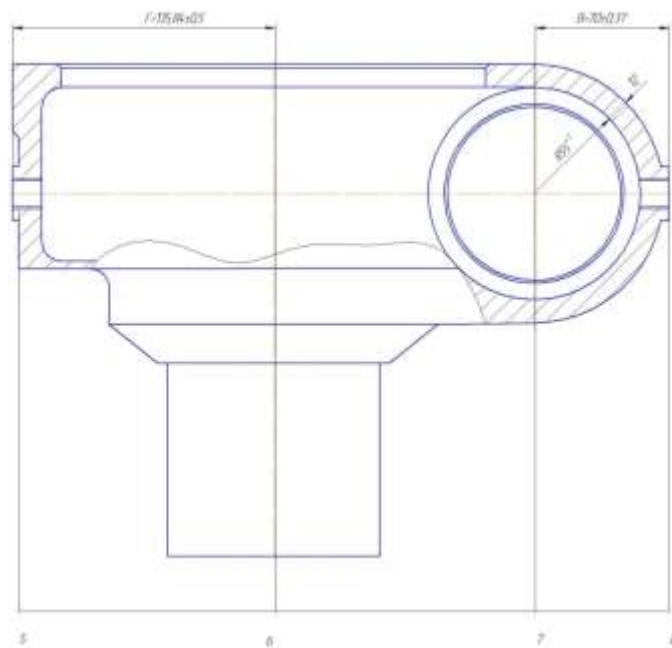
Преобразованный чертёж детали во второй проекции
